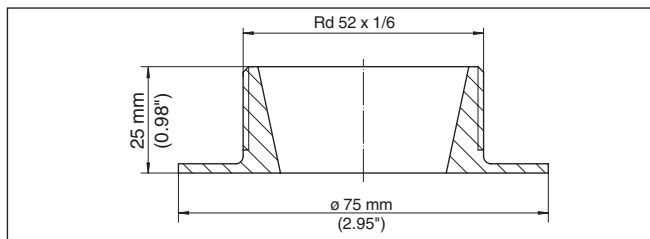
Dimensioni tronchetto a saldare attacco conico DN 25
